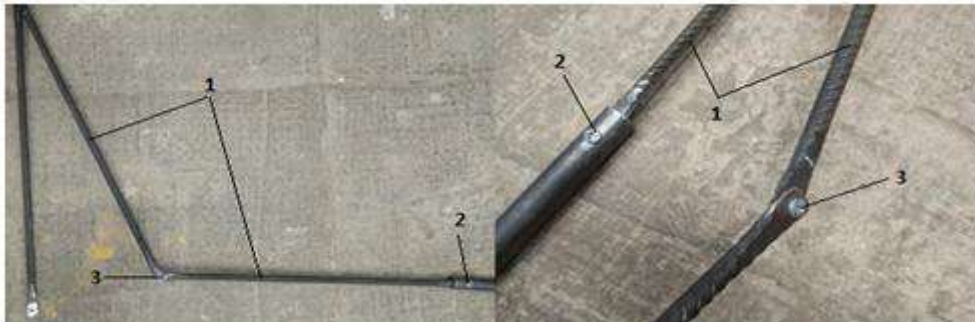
Штанги и узлы крепления: 1 – штанги; 2 – узел крепления штанг к желонке; 3 – шарнирное соединение штанг
